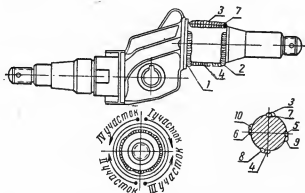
Восстановление коленчатой оси трактора ДТ-54.
